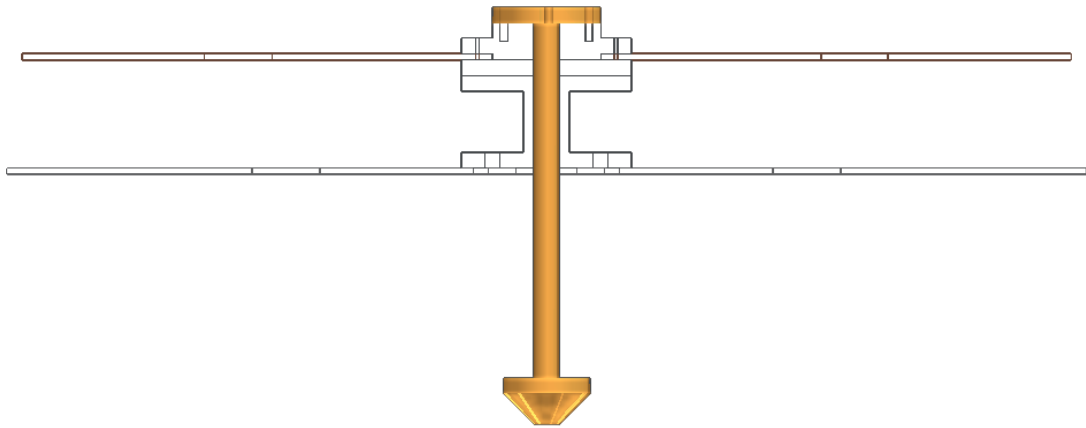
Eje del carrusel con engranaje cónico
